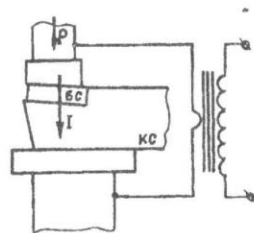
Схема контактной сварки на точечной машине
